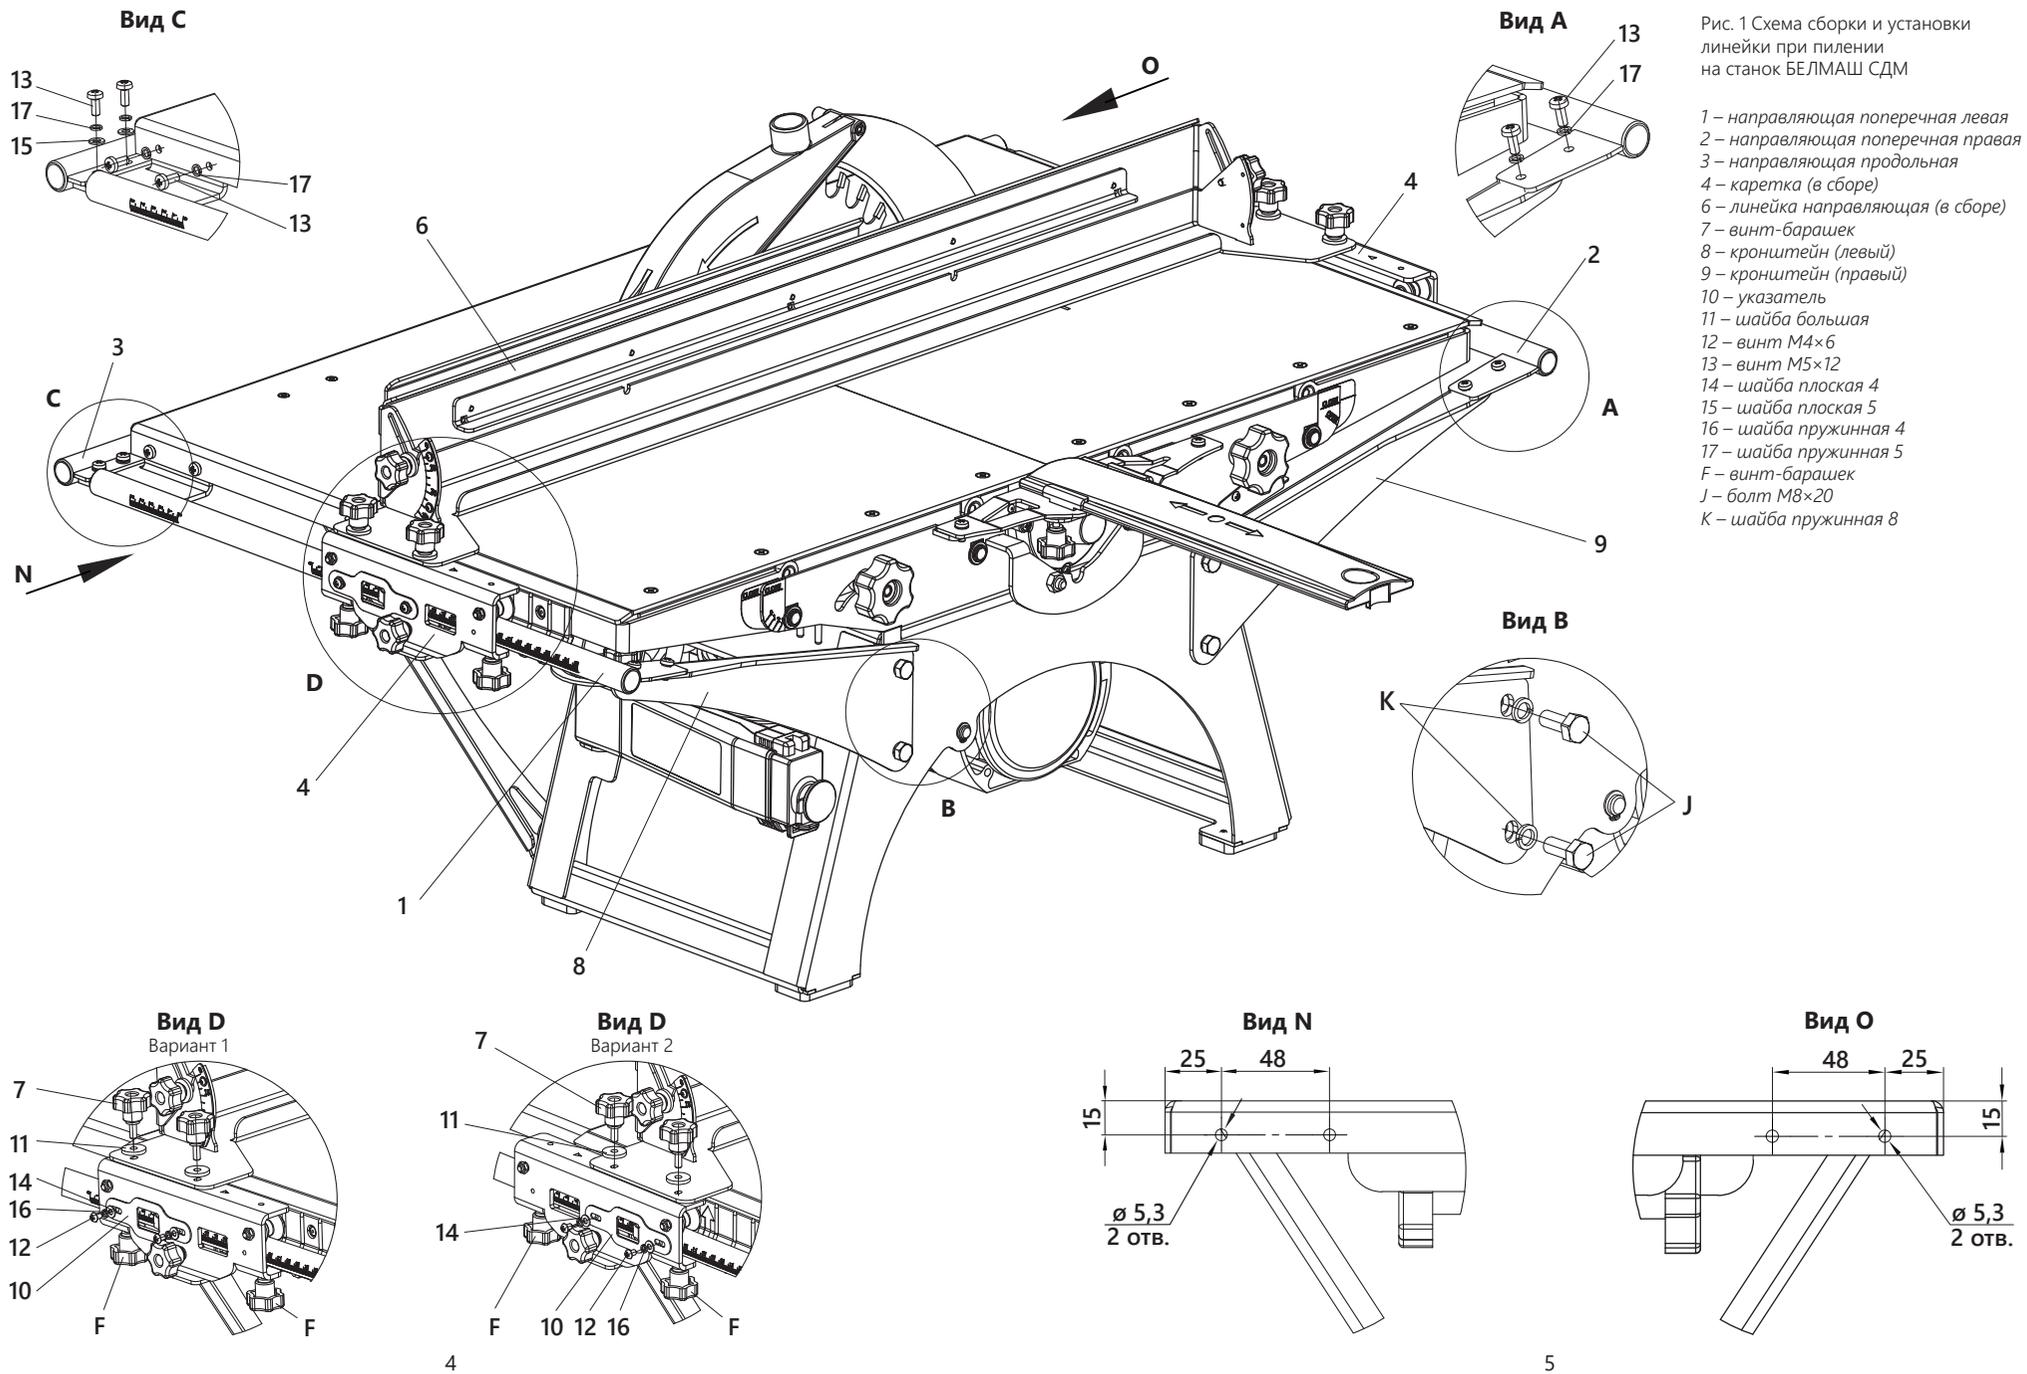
Схема сборки и установки линейки при пилении на станок БЕЛМАШ СДМ
